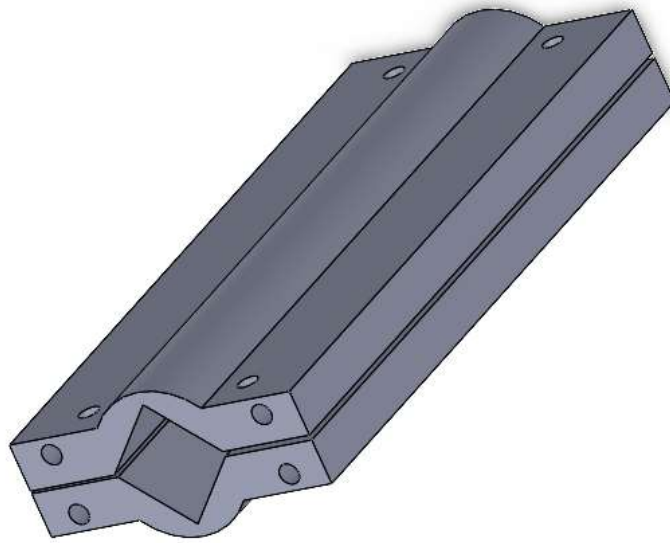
Оснастка для фрезерно центрівної операції
